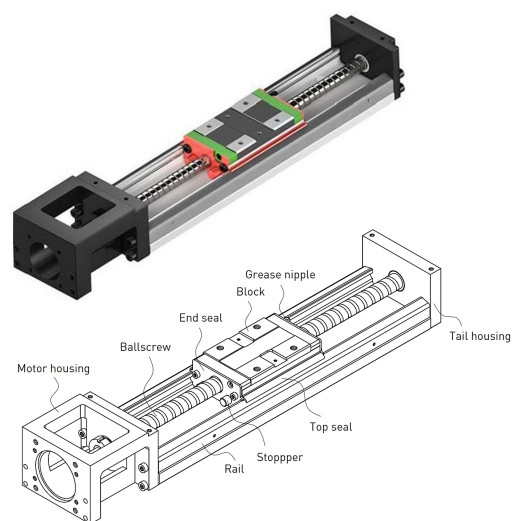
Robot de un eje KK5002P300A1F0 del fabricante HIWIN.
